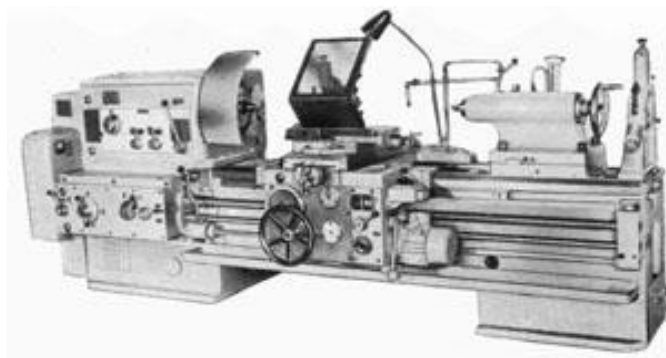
Токарный винторезный станок модели 1М63БФ101
